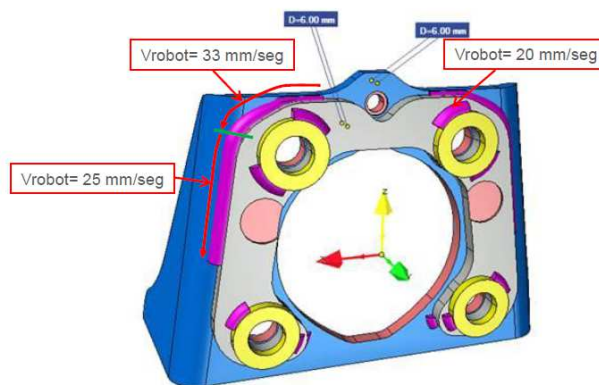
Velocidades de soldadura [Gestamp3 2015]
